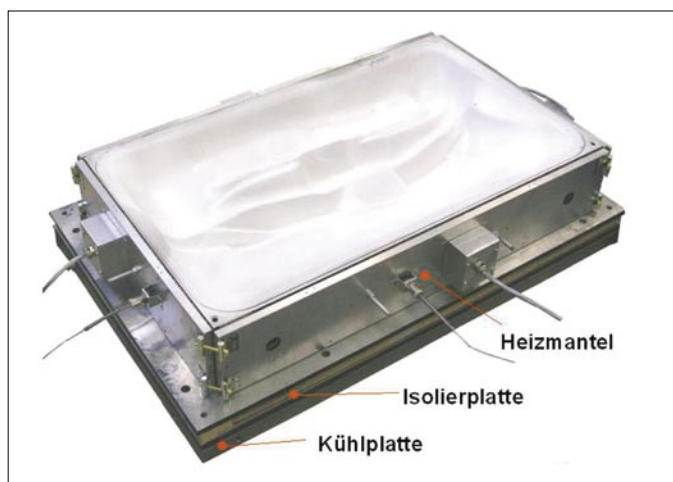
Werkzeug zum pneumatischen Tiefen einer Türinnenverstärkung
